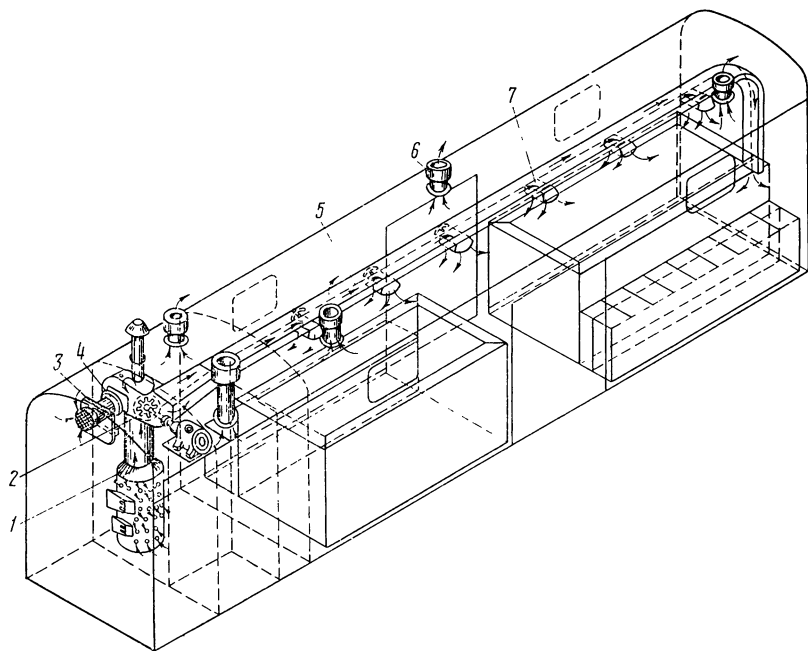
Схема вентиляции и отопления вагона для перевозки живой рыбы
